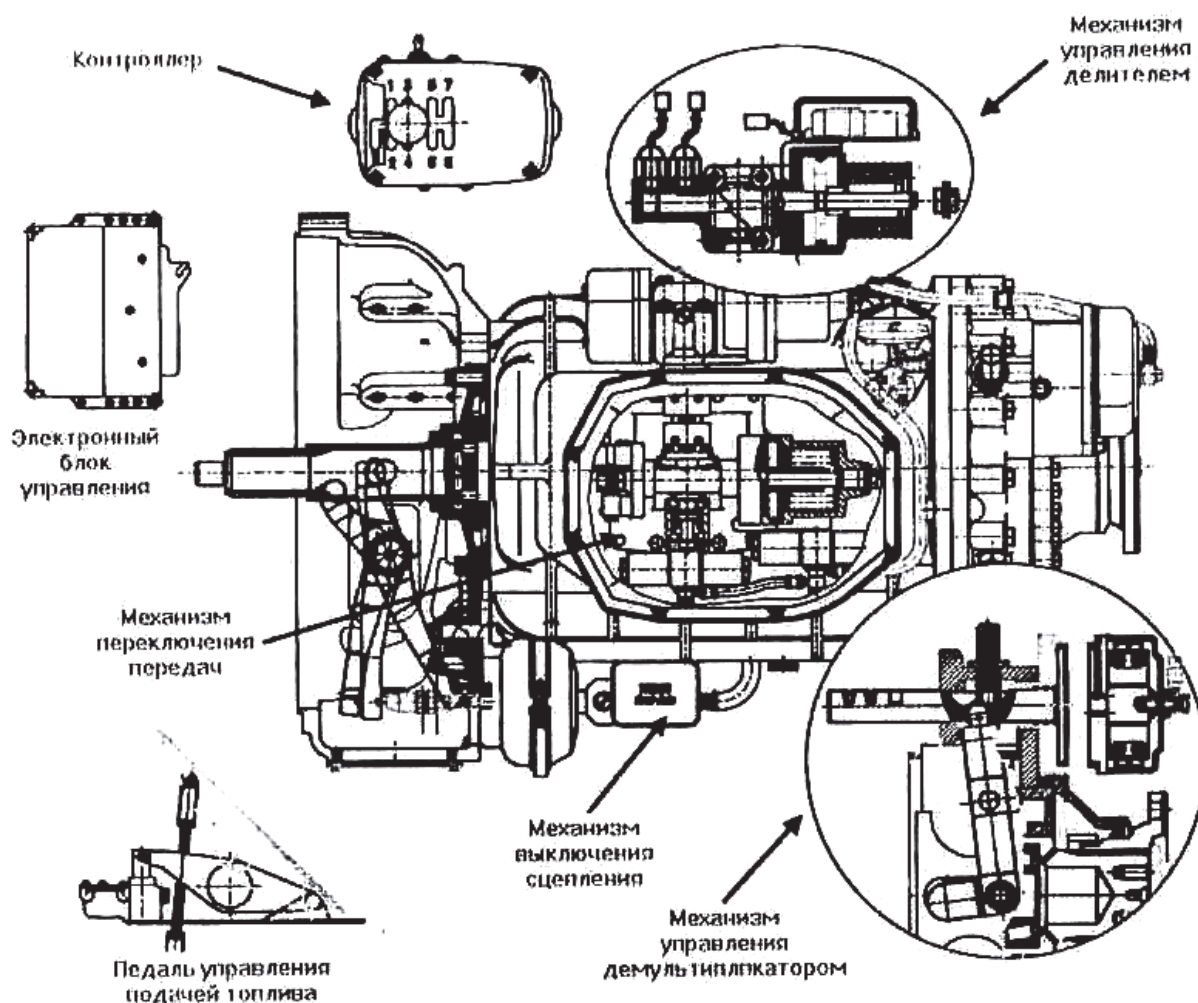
Схема полуавтоматического управления коробки передач ТМ16-2000
